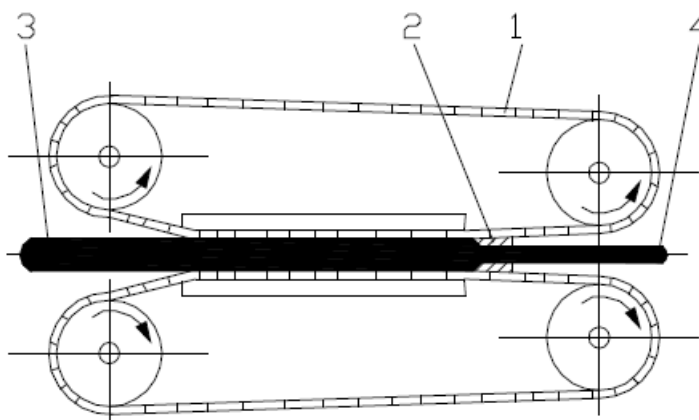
Схема процесса непрерывного прессования способом Лайнекс: 1- приводные цепи; 2 – матрица; 3 – матрица; 4 – изделие
